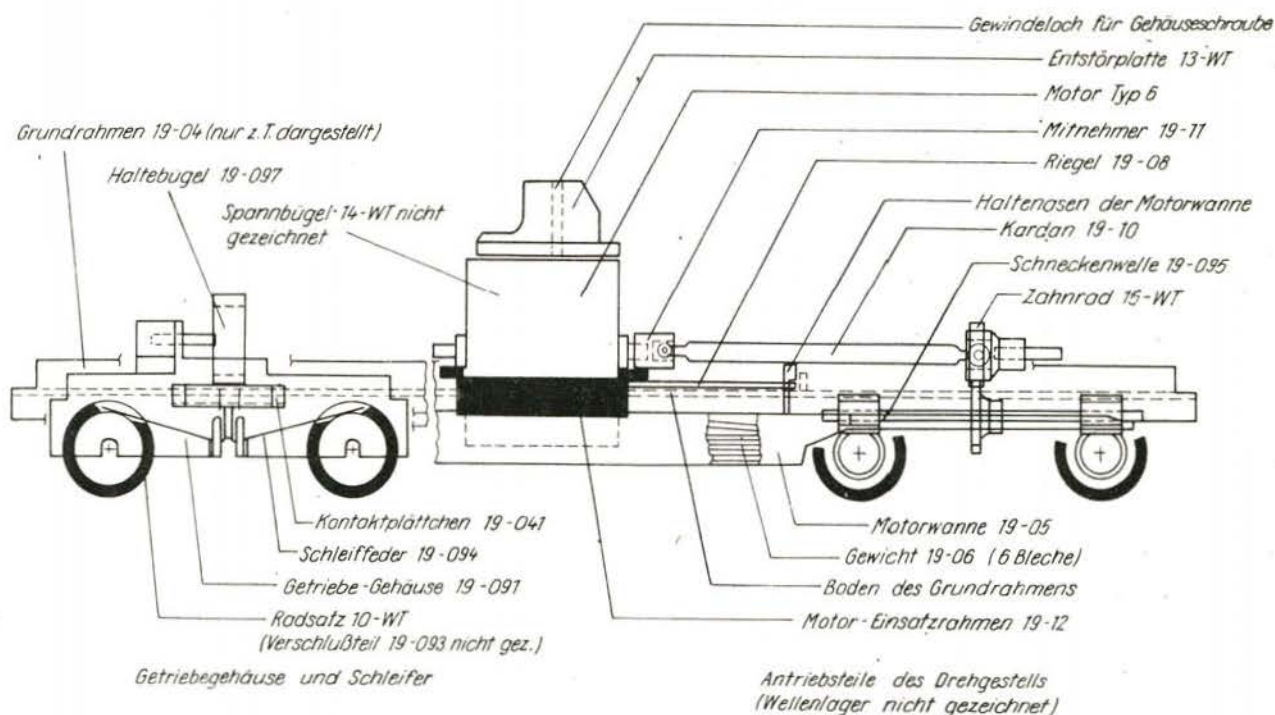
Antriebs- und Montageschema des H0-Modells (Ausführung ab Anfang 1974)
